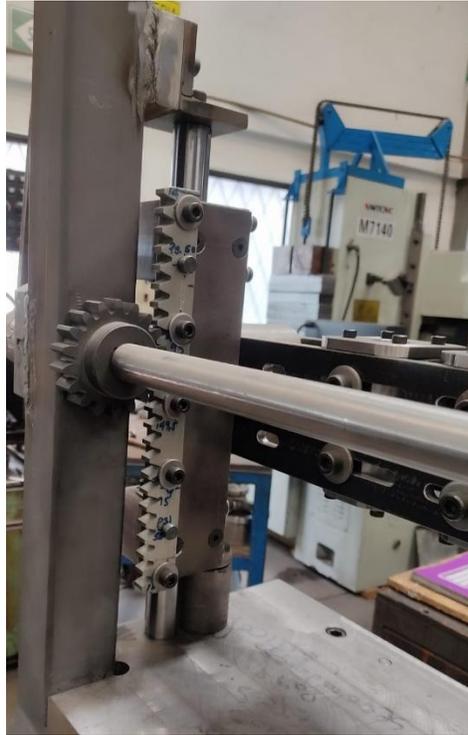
Montaje de cremallera. Fuente: Autor.
